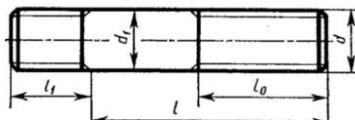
Чертеж шпильки:  $d$  – диаметр резьбы;  $d_1$  – диаметр средней части;  $l$  – длина шпильки;  $l_1$  – длина ввинчиваемого конца;  $l_0$  – длина резьбы внешнего конца
